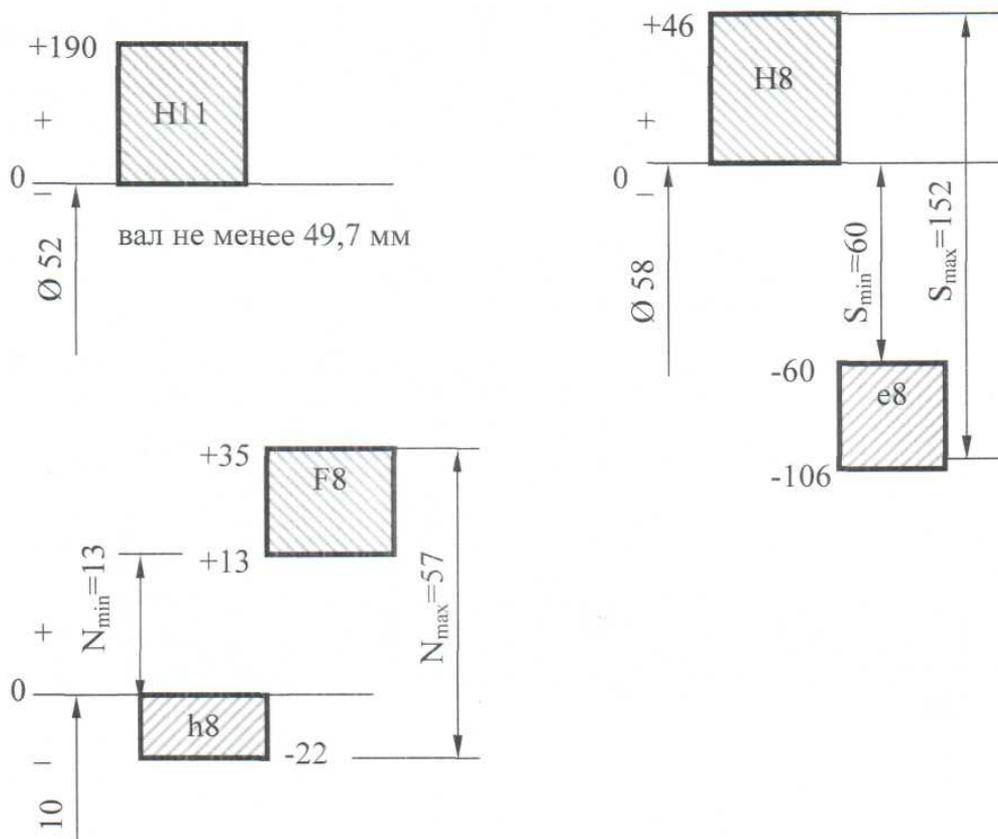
Схема полей допусков деталей шлицевого соединения
